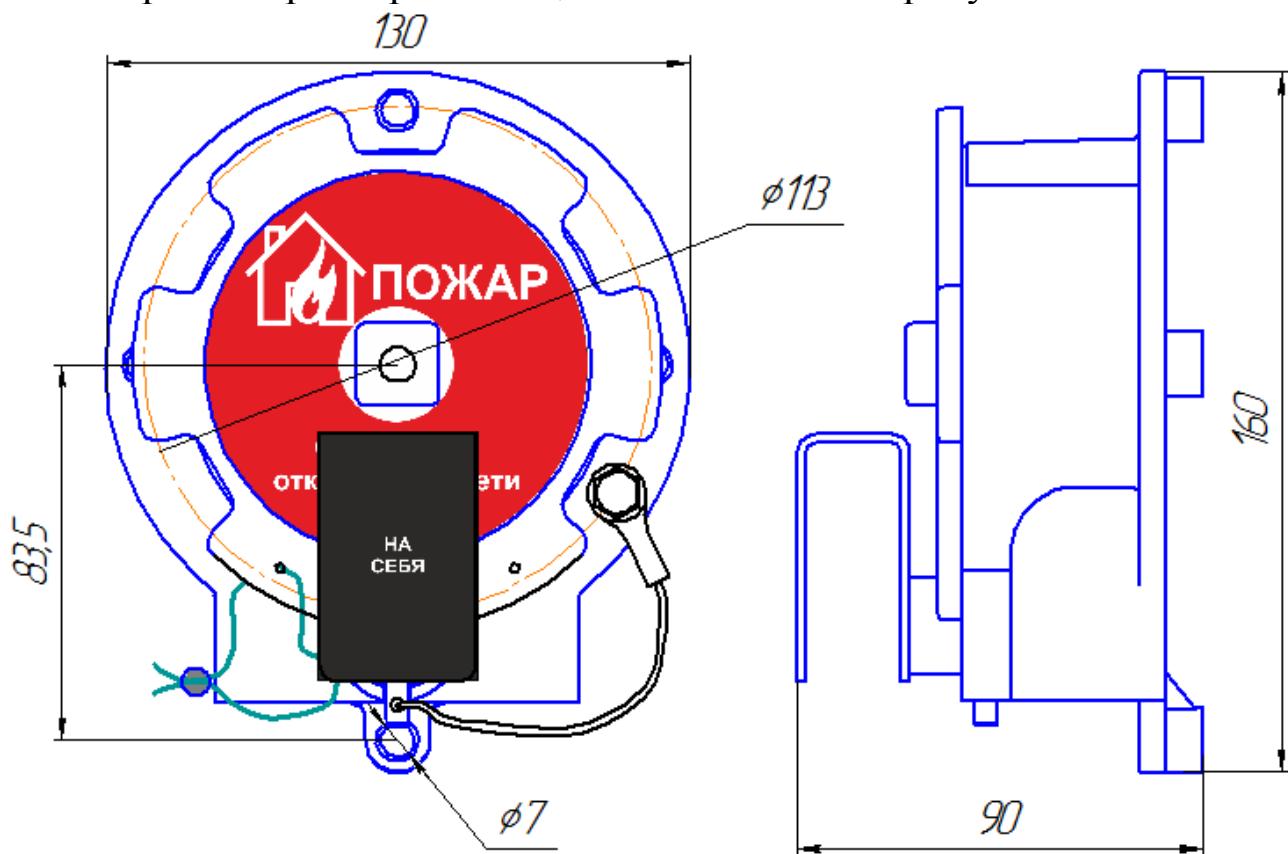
Извещатель пожарный ручной взрывозащищенный
